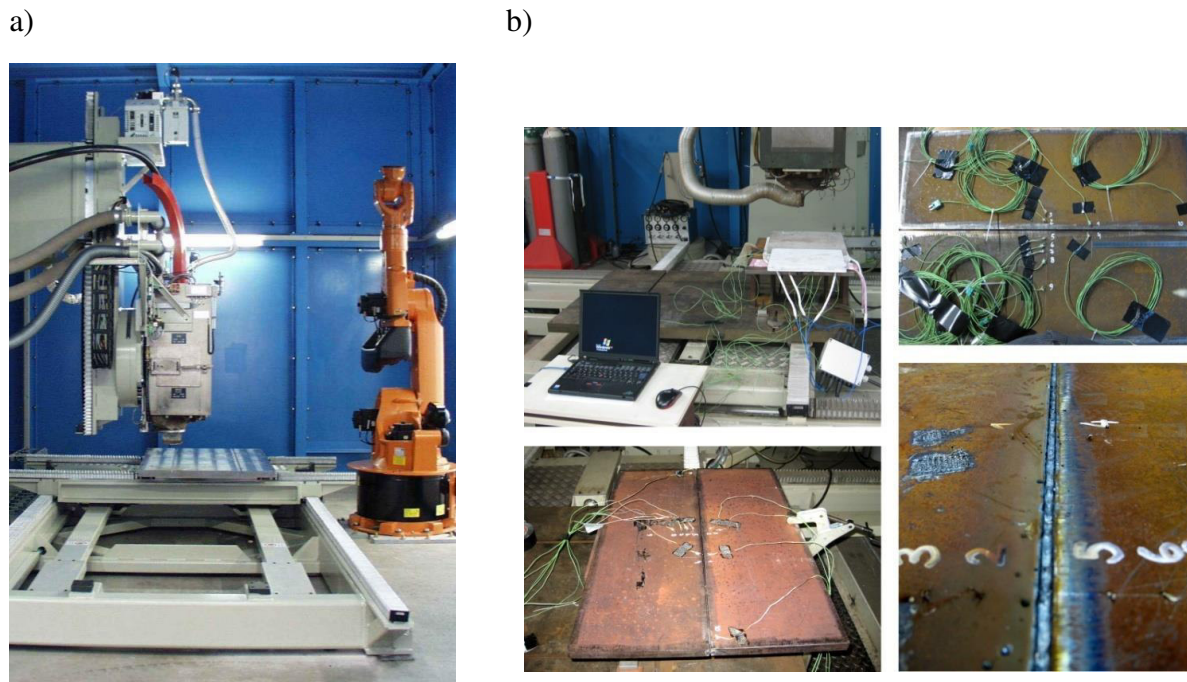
a) Anlage zum Elektronenstrahlschweißen Typ NVEBW 25-175 TU der Firma PTR-Präzisionstechnik GmbH mit Verfahrenseinheit und Röntgeneinhausung am Institut für Werkstoffkunde, Leibniz Universität Hannover
